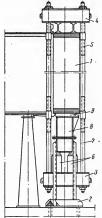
Опрессовочный стенд. 1— обод ротора; 2— опора; 3— нижняя нажинная балка; 4— верхняя нажинная балка; 5— шпялька; 6— домкраты; 7— опоравя рама; 8— подставк; 9— тормозняя плять.
